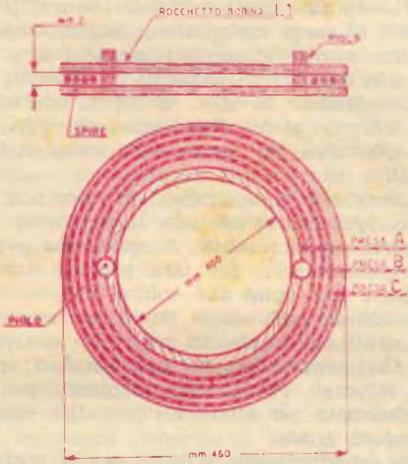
Dimensioni della bobina oscillatrice L1.
